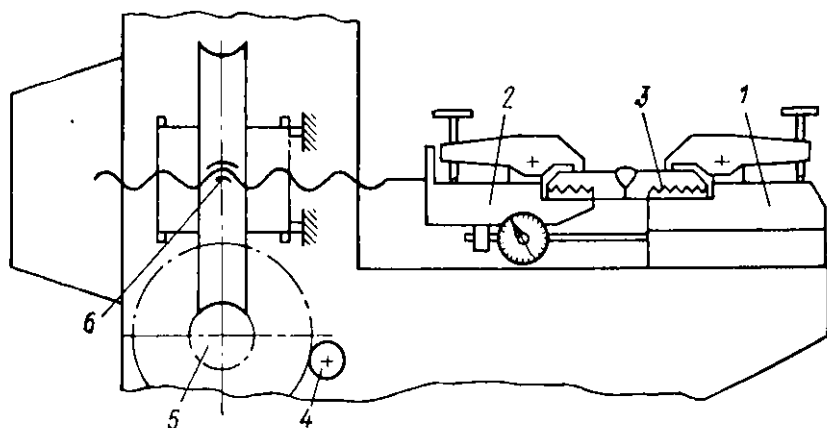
Схема машины ЛТП-6 для испытаний на горячие трещины при сварке:
